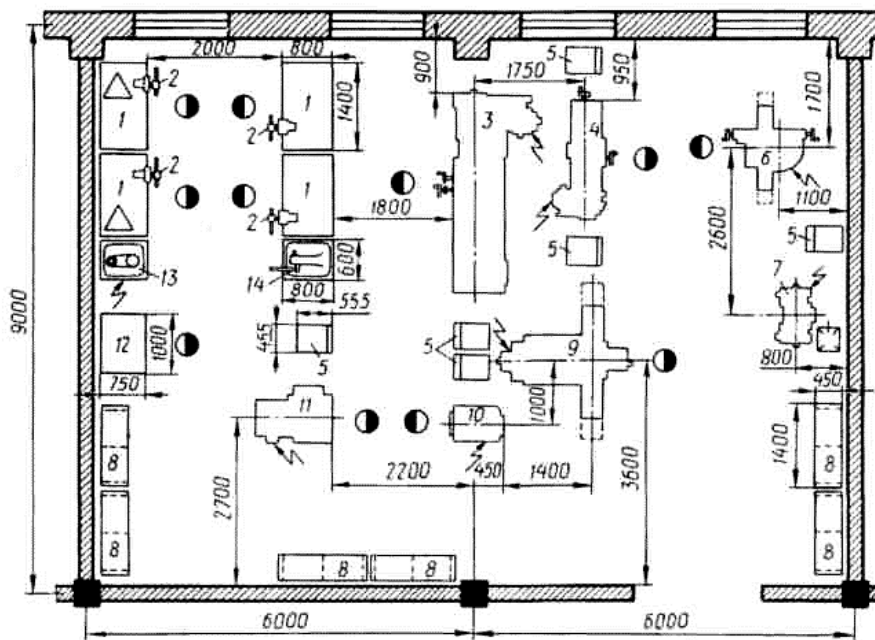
Слюсарно-механічне відділення ПАТ: 1 - слюсарний верстак; 2 - слюсарні ле- щата; 3, 4 - токарно-гвинторізні верстати; 5 - інструментальна шафа; 6 - універсально-заточний верстат; 7 - обдирно-шліфувальний верстат; 8 - стелаж для деталей; 9 - універсально-фрезерний верстат; 10 - верстат відрізний; 11 - вертикально-сверлильний верстат; 12 -перевірочна плита; 13 - настільно-свердлувальний верстат; 14 - прес з ручним приво- дом
